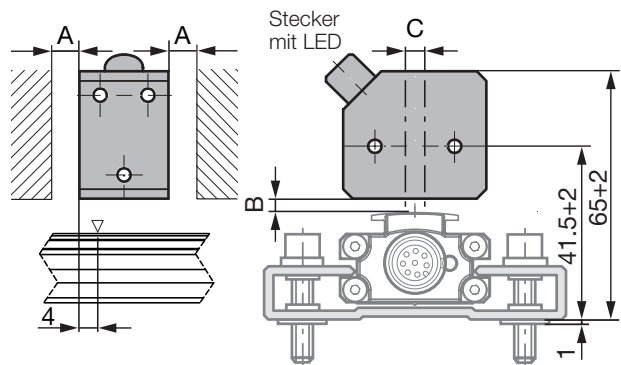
Maße und Abstände mit Positionsgeber BTL5-P-4500-1 mit elektrischer Magnetfeld-Erzeugung (24 V/100 mA)
